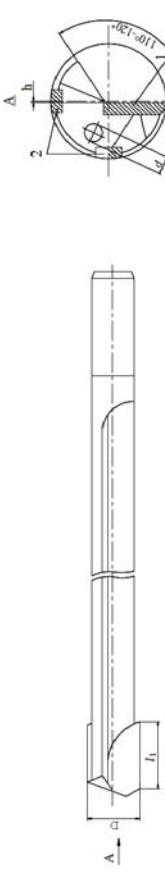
Ружейное сверло с присоединенными режущей и направляющими элементами
